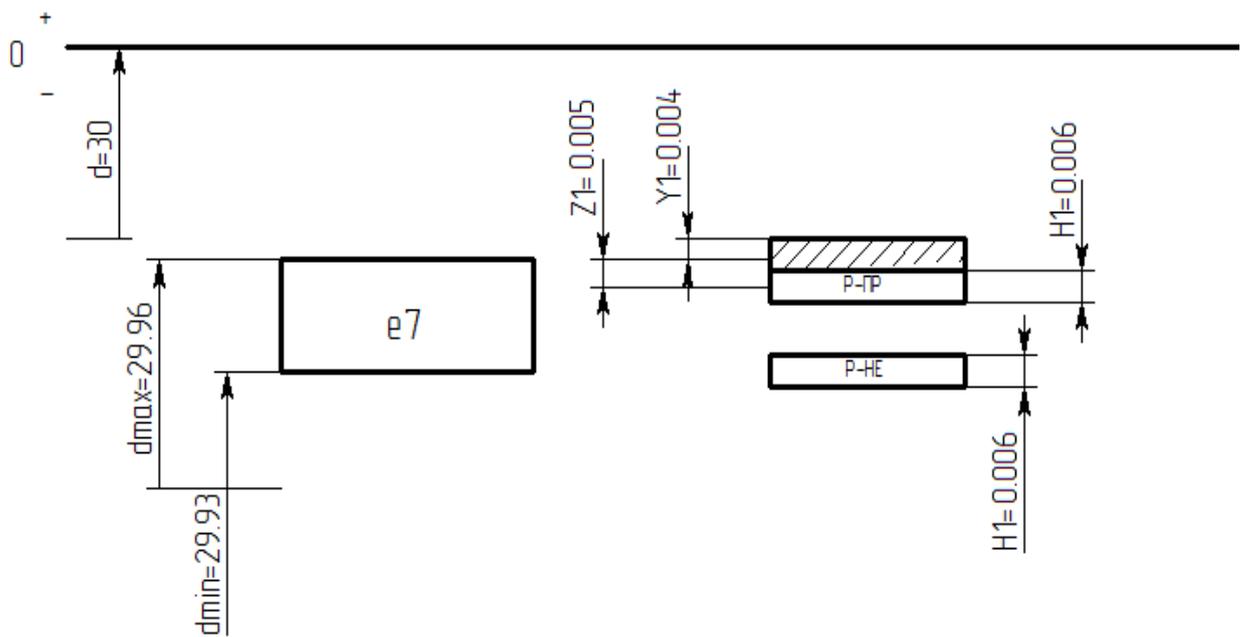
Схема расположения полей допусков калибра – скобы
